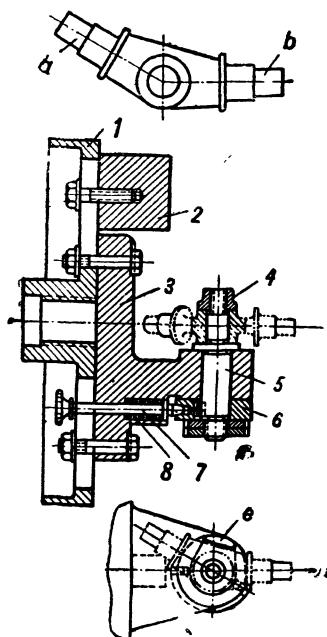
Поворотное приспособление для обработки концевых шеек изделия.
